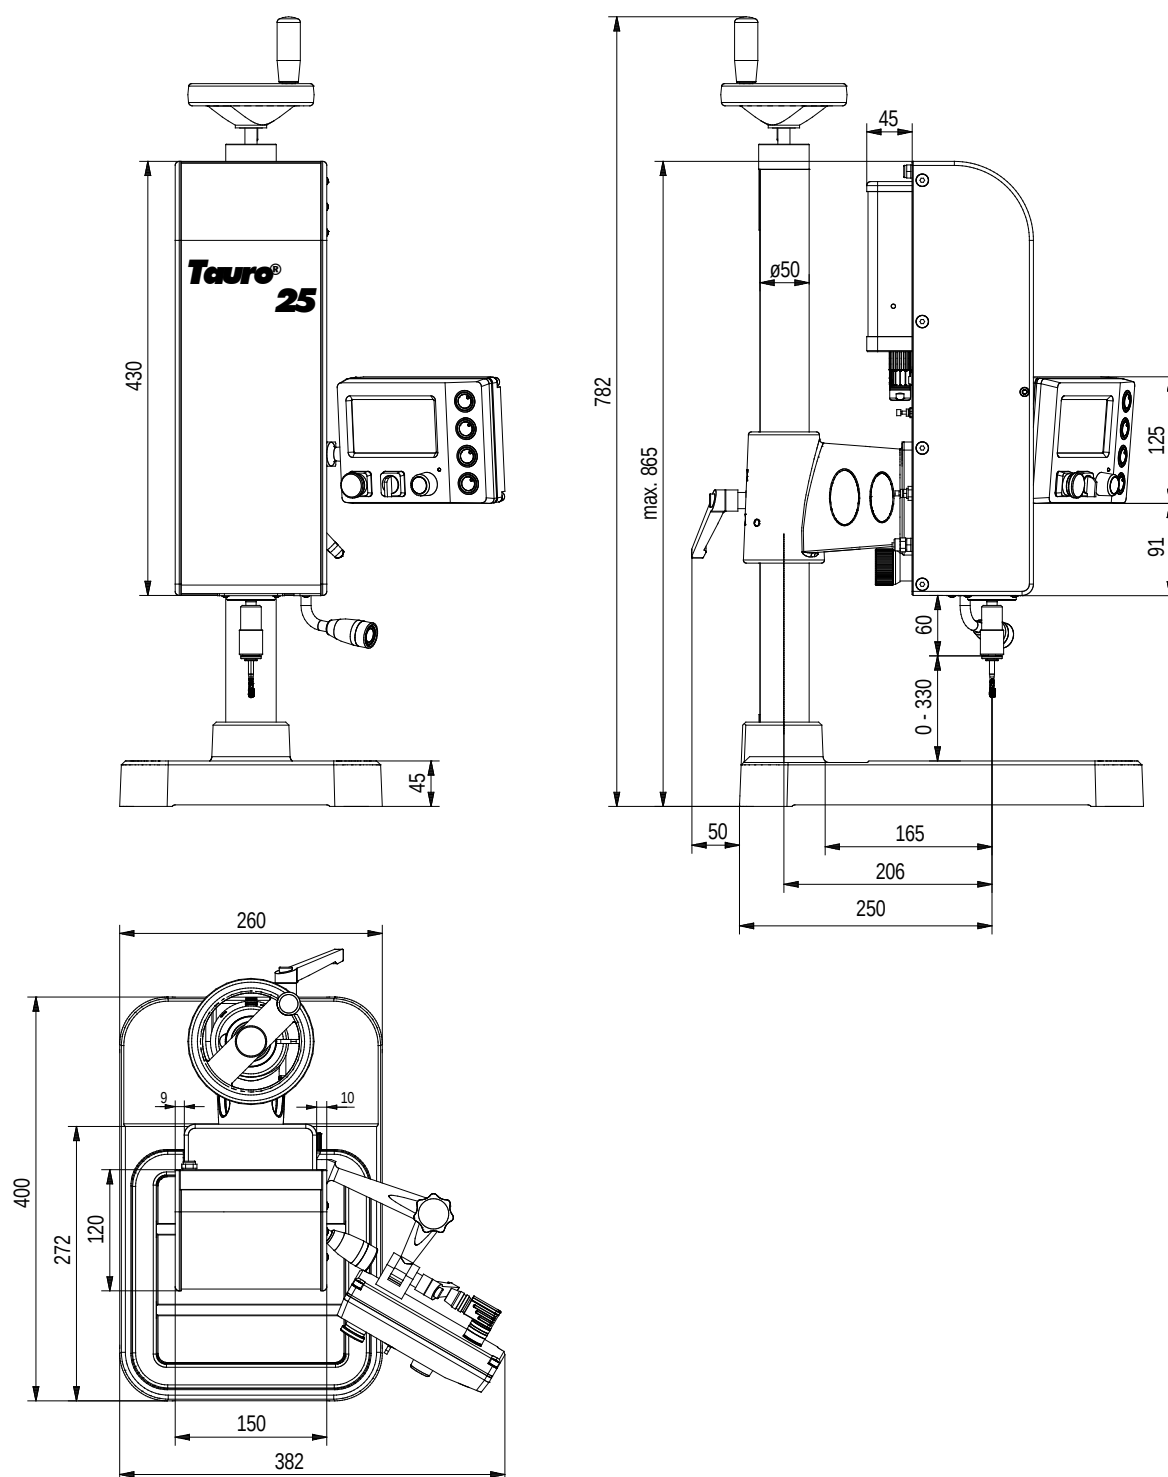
Vues de la machine à usiner les filets Tauro 25
